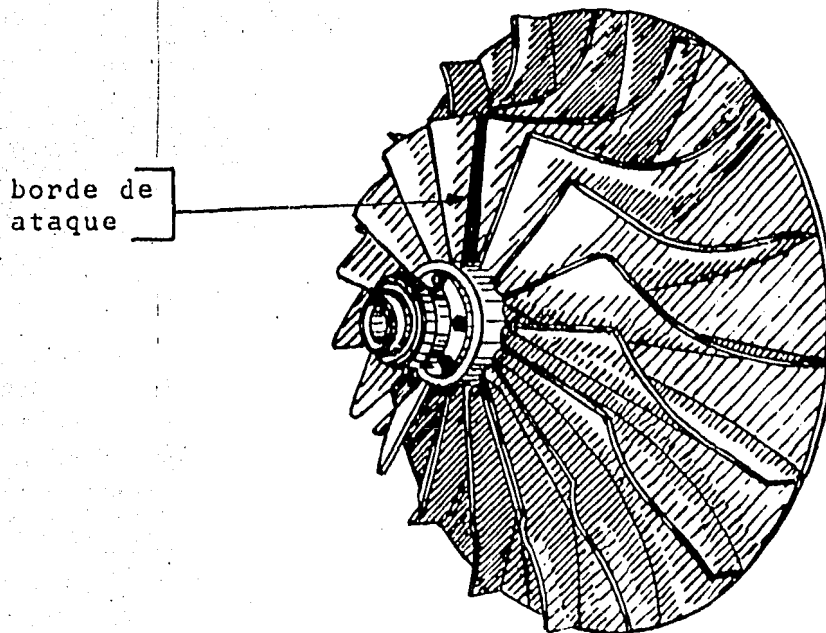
BORDE DE ATAQUE DEL ALABE DE UN COMPRESOR CENTRIFUGO
